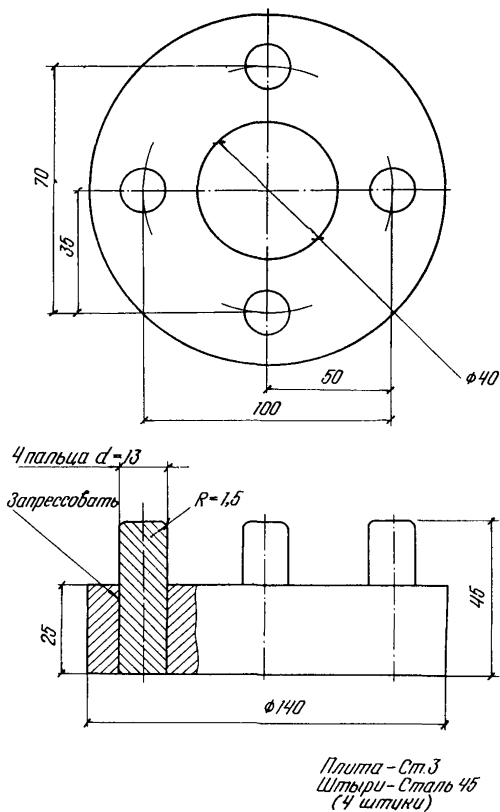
Кондуктор для сборки и сварки образцов, предназначенных для испытания на отрыв точки
